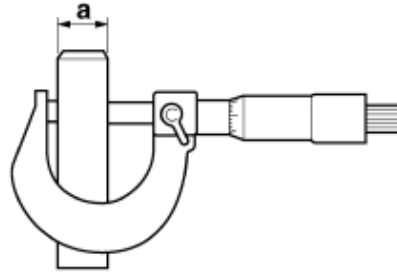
Pengukuran Dimensi *Camshaft
